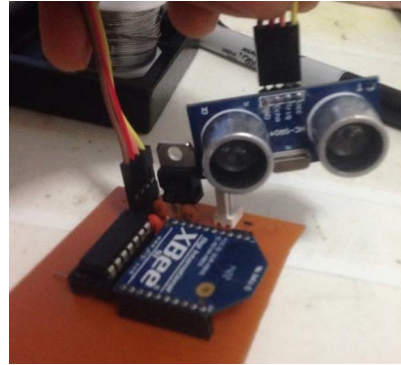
Diseño PCB de circuito:Ultrasónico.
